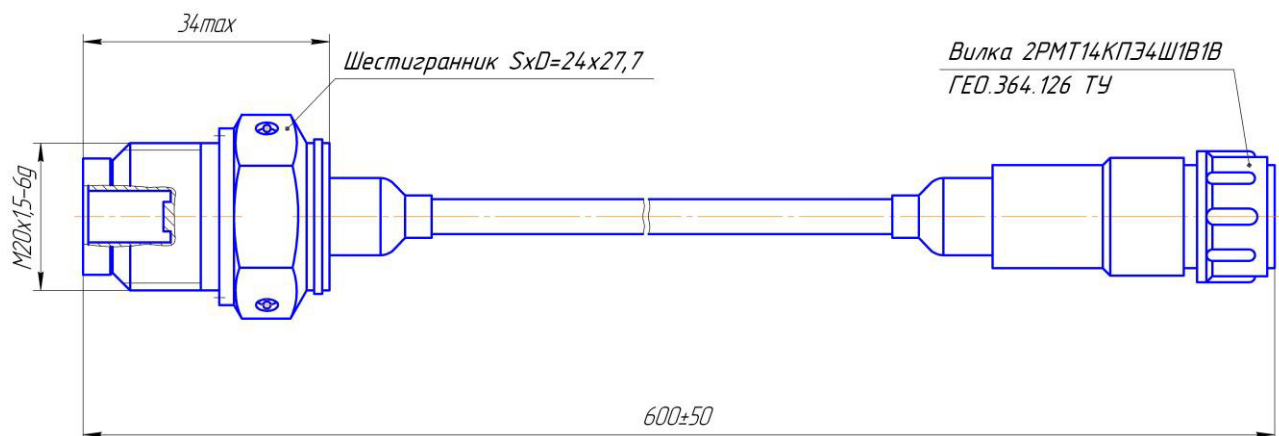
Габаритные и установочные размеры датчика ДДВ 015
